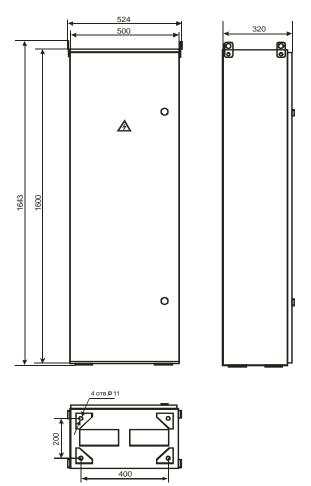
Внешний вид, габаритные и установочные размеры корпуса шкафа силового ШРС1-XX-5-Узола.
